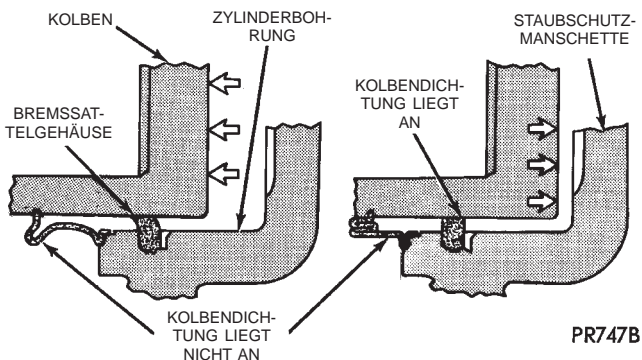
Kompensierung des Verschleißes der Bremsbeläge durch die Kolbendichtung
